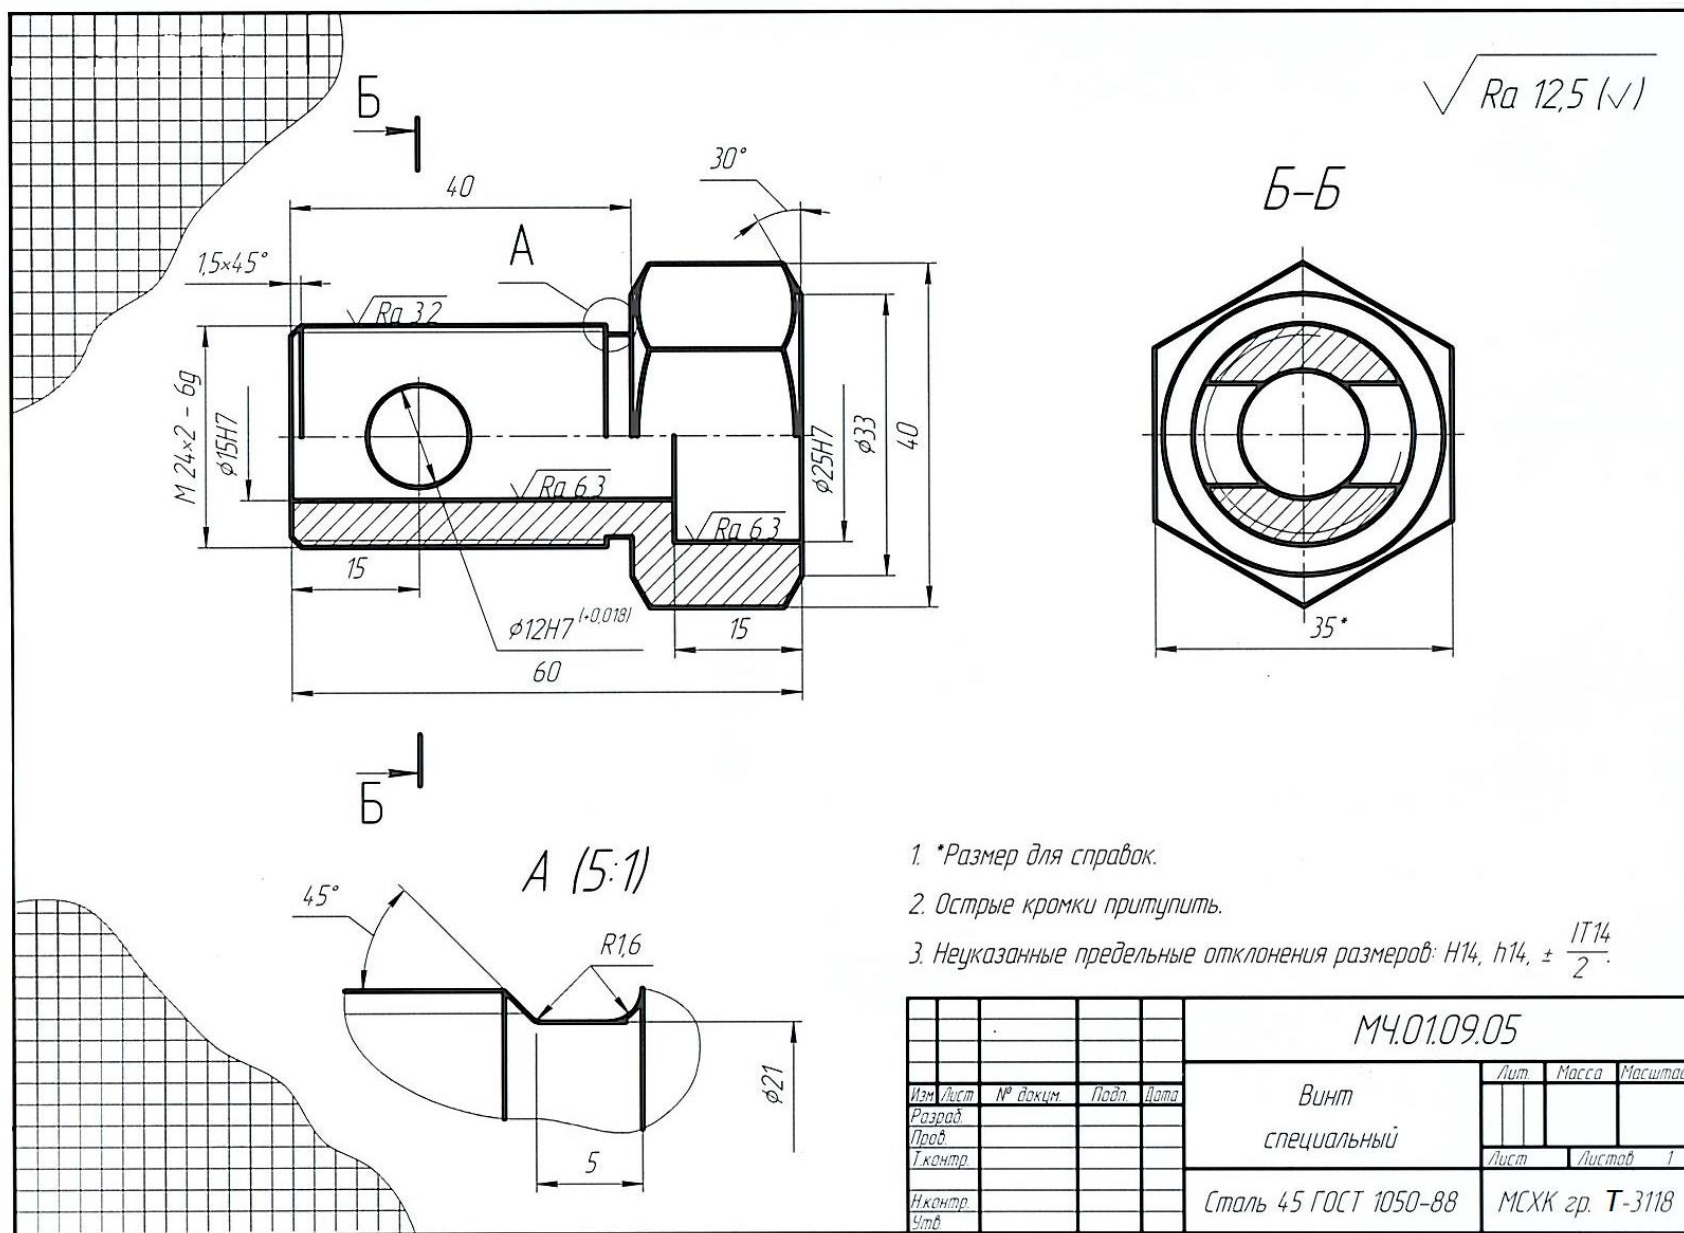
Образец выполнения листа 6 – Эскиз детали
